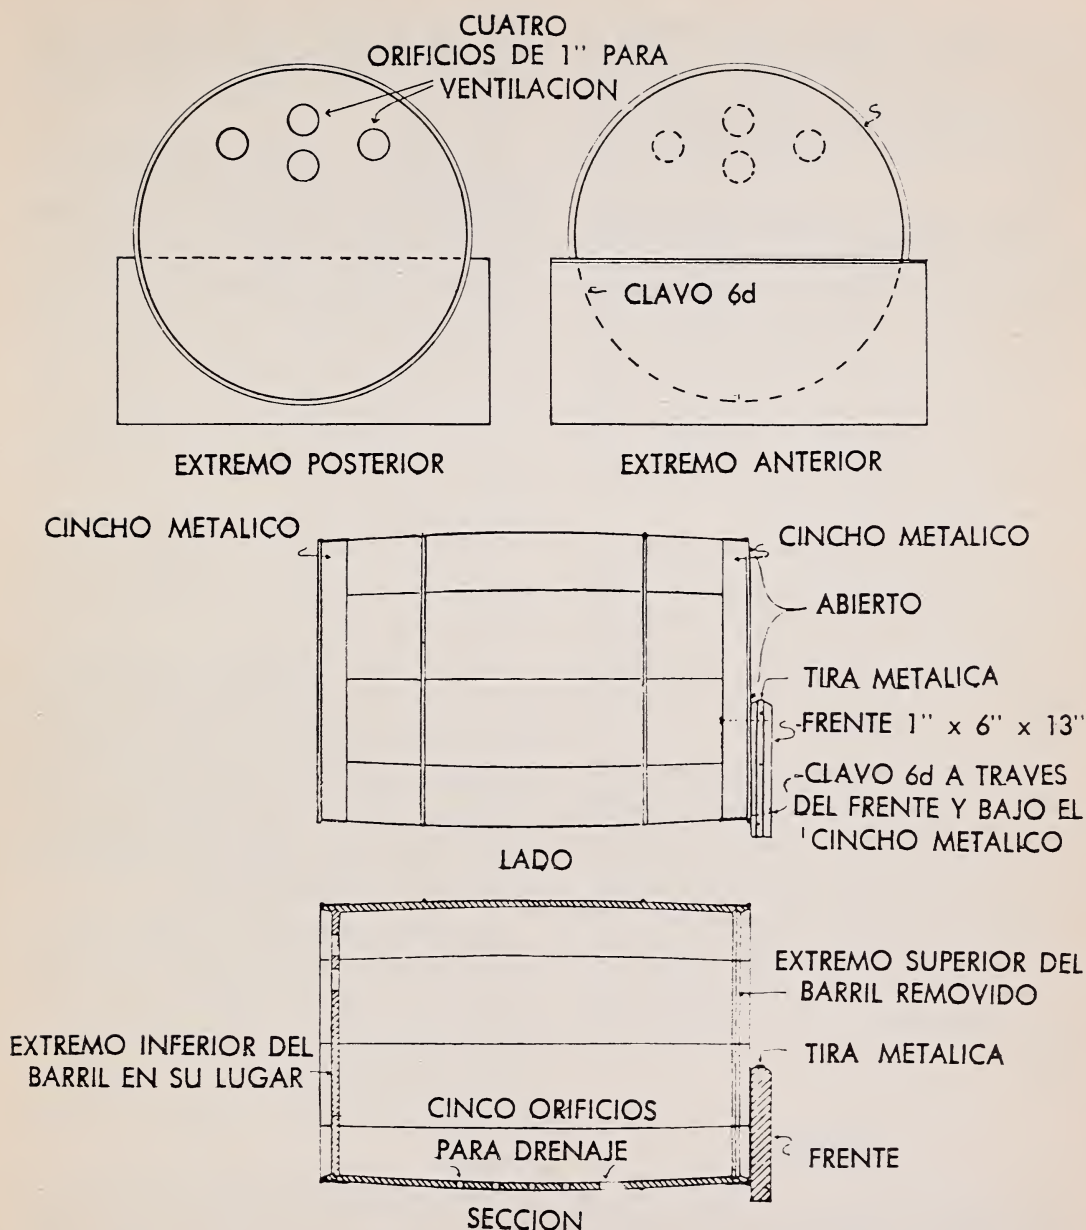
Detalles para la construcción de un nido, con un barril de clavos.
